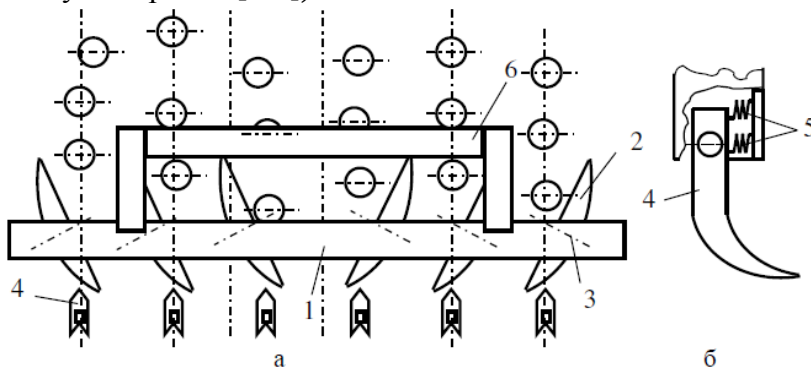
Конструктивна схема а – копача для викопування коренеплодів цикорію: 1 – рама; 2 – сферичний диск; 3 – вісь диска; 4 – розрихлювач; 5 – пружина; 6 – сниця; б – схема кріплення лапи
